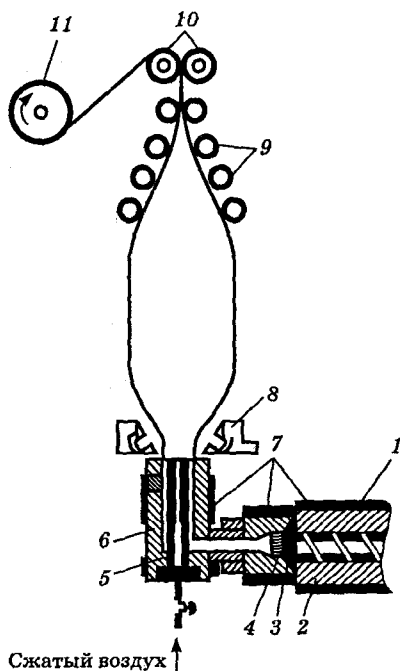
Схема изготовления пленки раздуванием трубы вверх:
